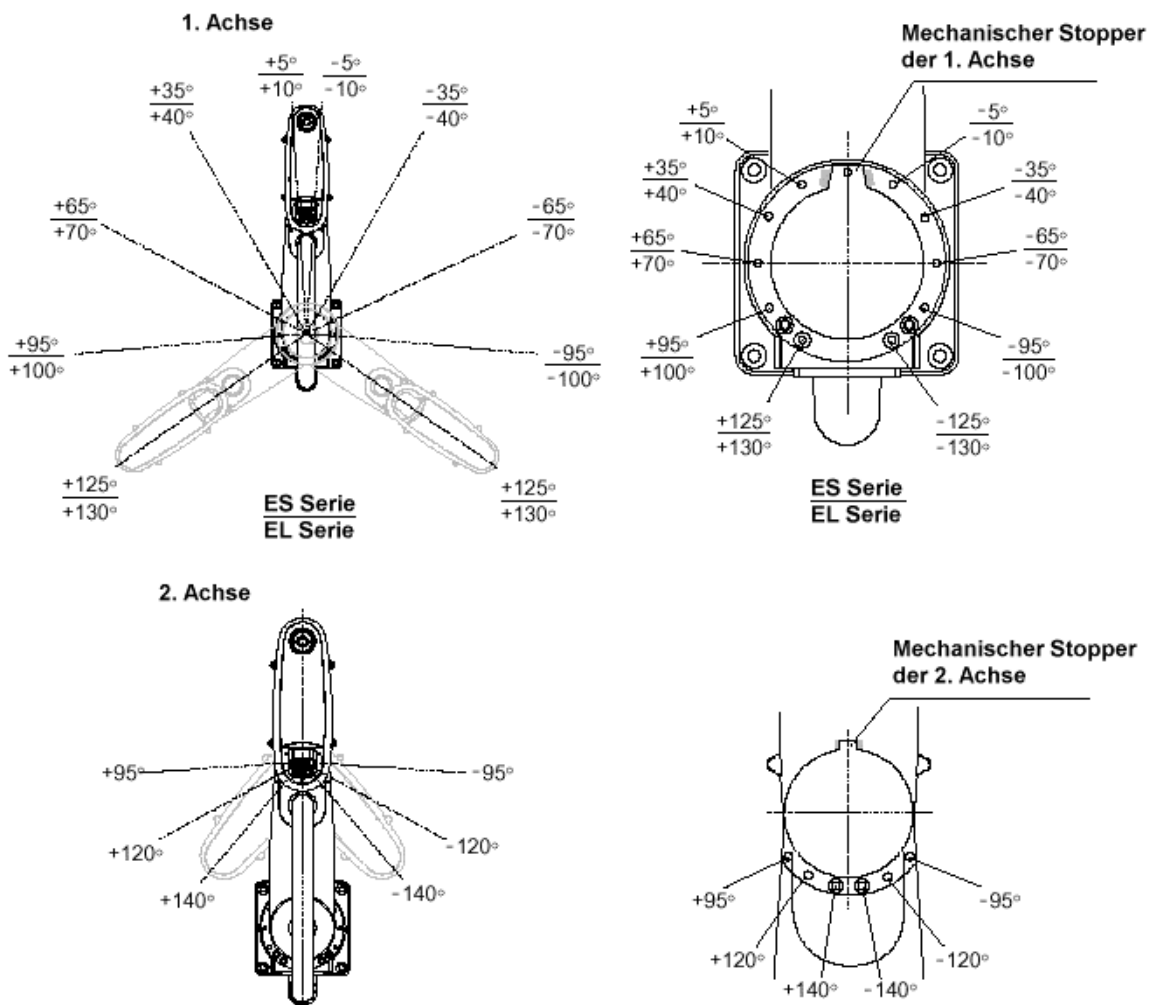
Gewindebohrungen, um die Position des mechanischen Stoppers zu verändern
